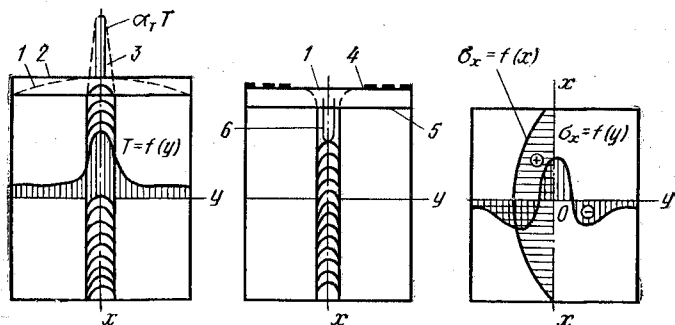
Процесс возникновения сварочных напряжений при сварке пластины встык:
